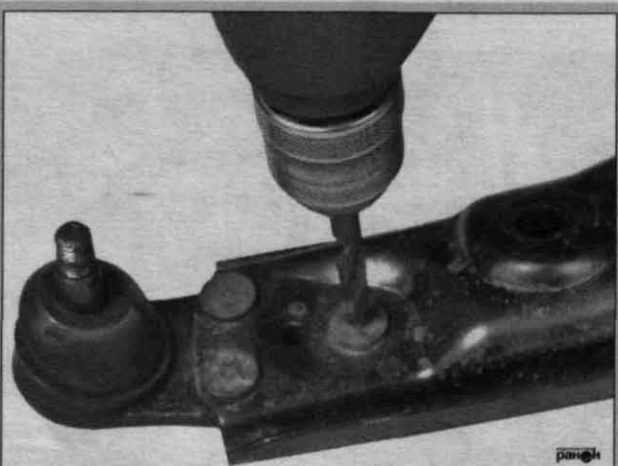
Высверливание заклепок крепления шаровой опоры
